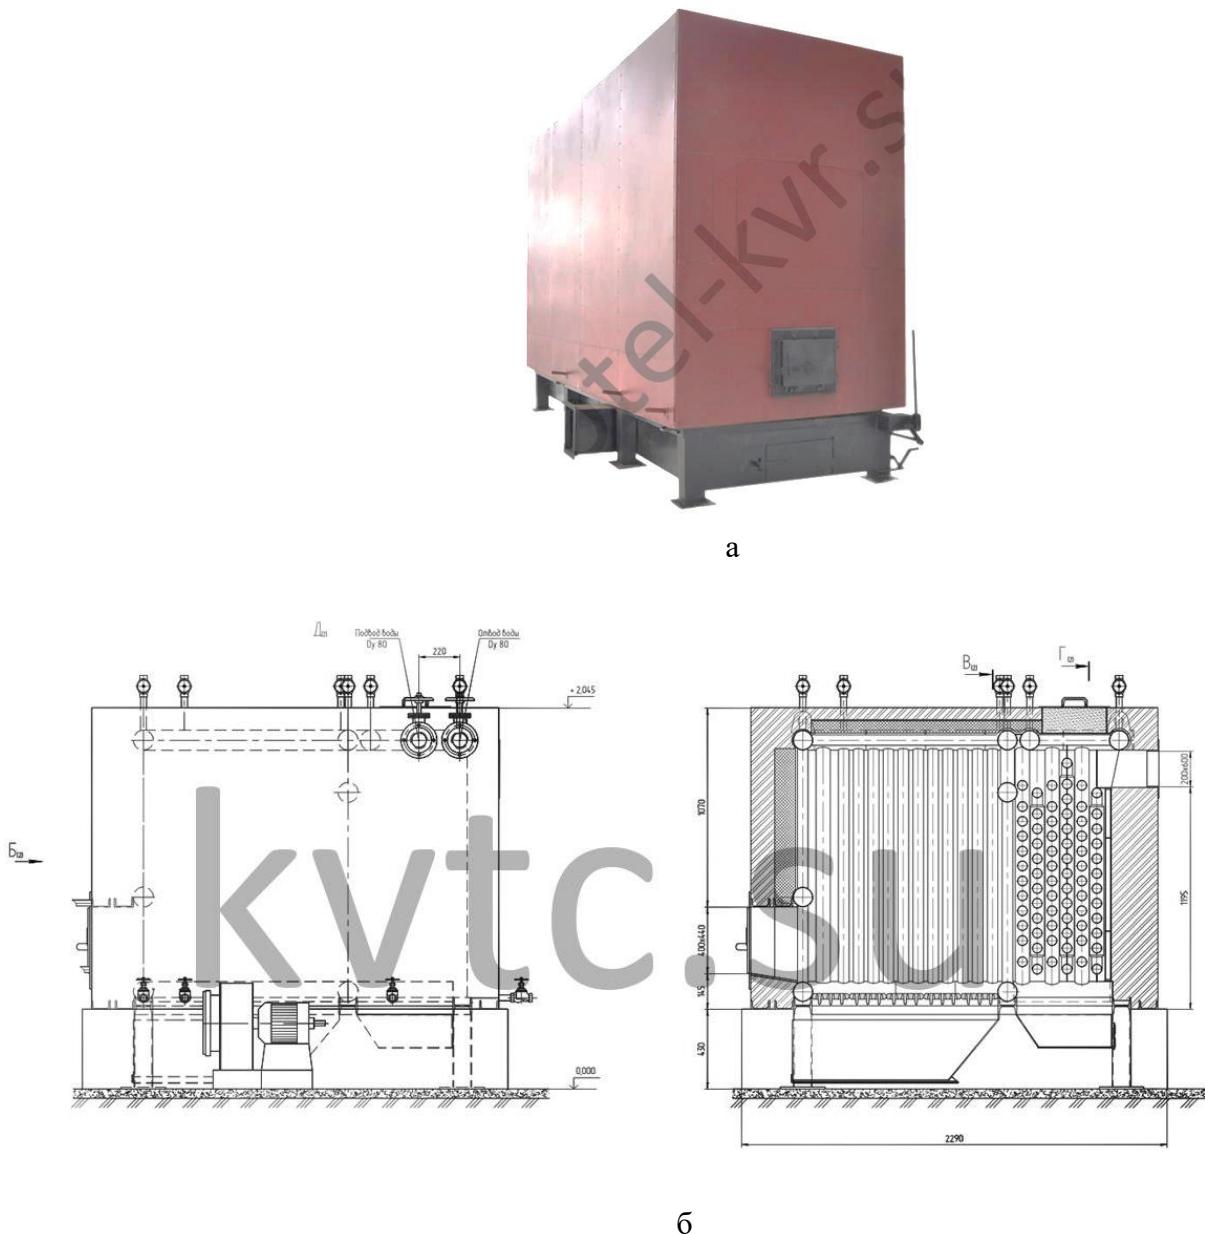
Устройство котла КВр: а) общий вид котла; б) чертеж котла
